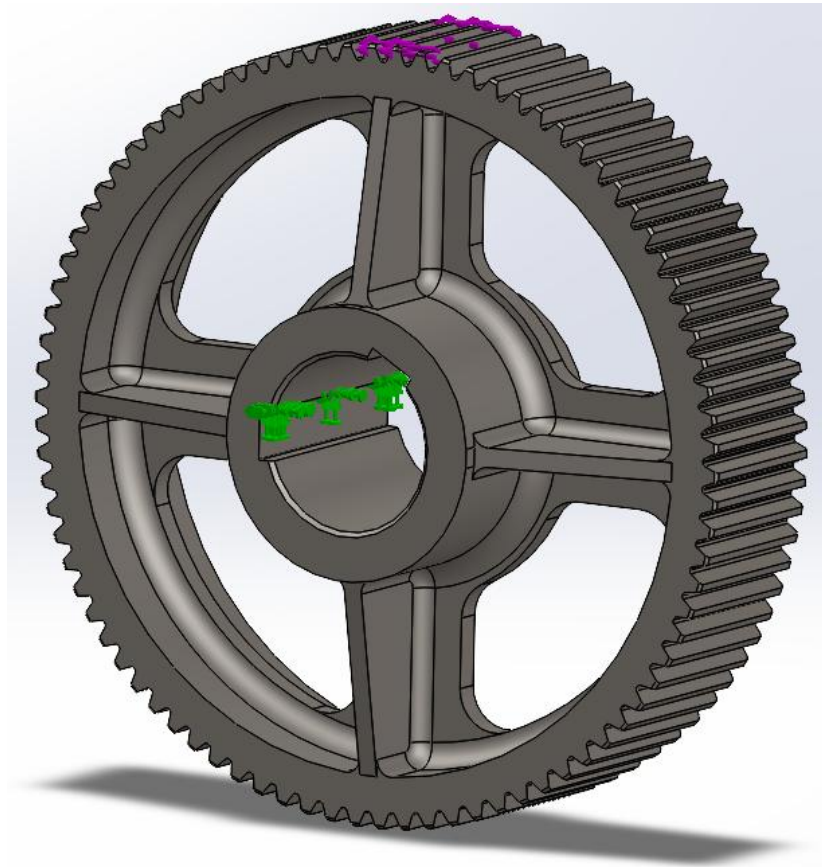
Тривимірна розрахункова модель зубчастого колеса циліндричного редуктора в середовищі SolidWorks Simulation
